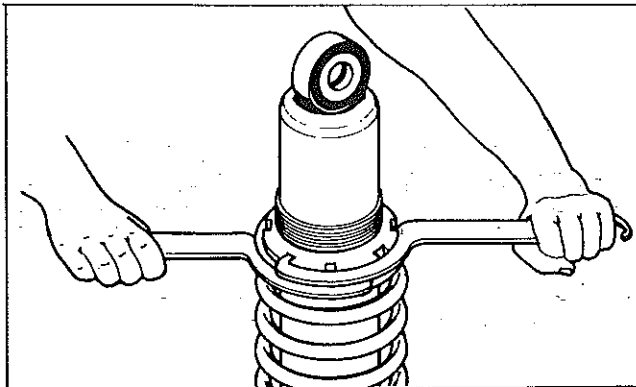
DESMONTAGEM DO AMORTECEDOR
